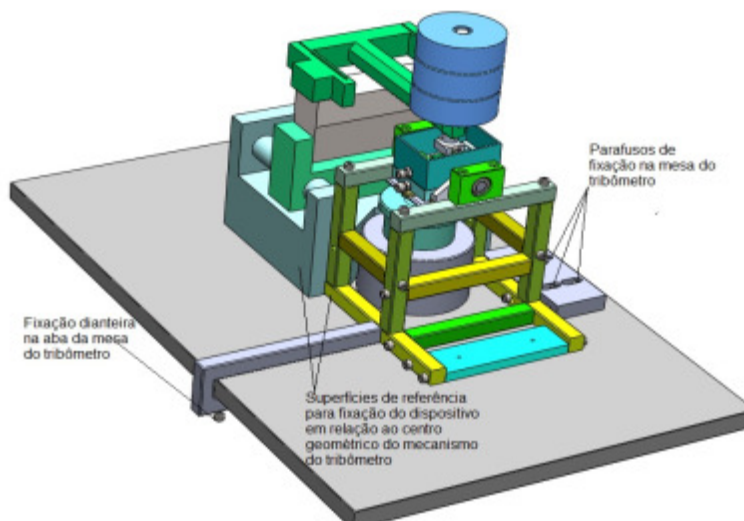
Posição dos parafusos de fixação e superfícies de referência de montagem no acoplamento do dispositivo no gabinete do tribômetro.
